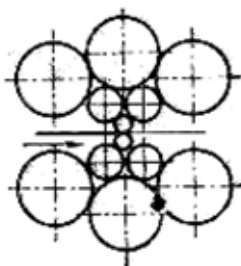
Схема расположения валков в 12-валковой клетке
